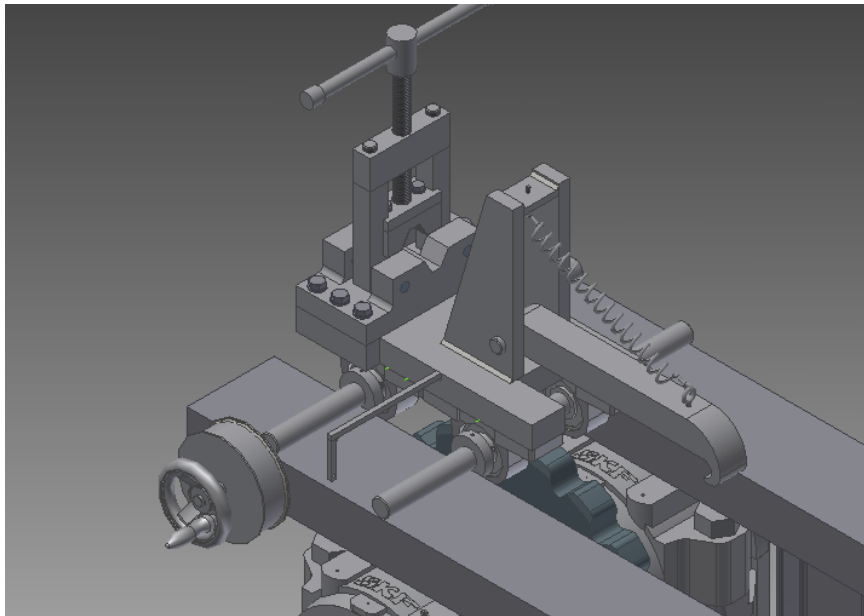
Disposición del sistema de retorno en el ensamblaje de la máquina.
